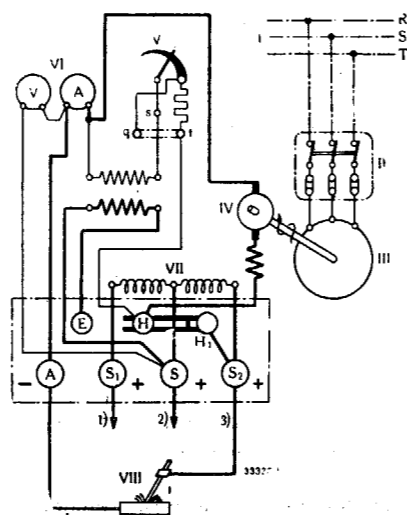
º—Esquema del grupo de soldadura universal para un soldador.
